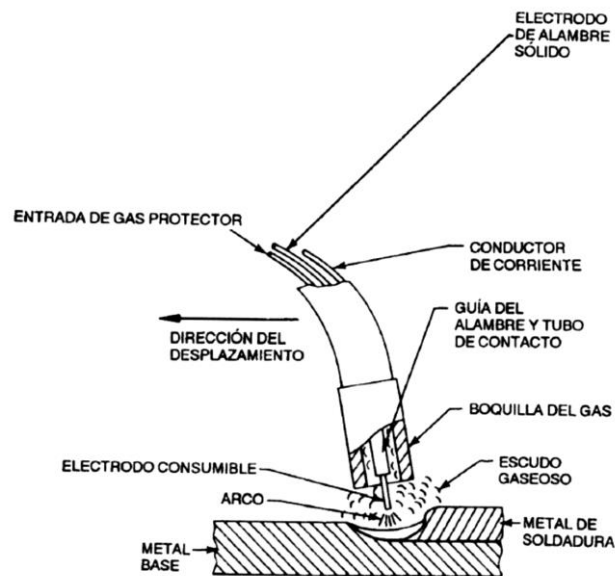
Esquema del proceso de soldadura GMAW [10].
